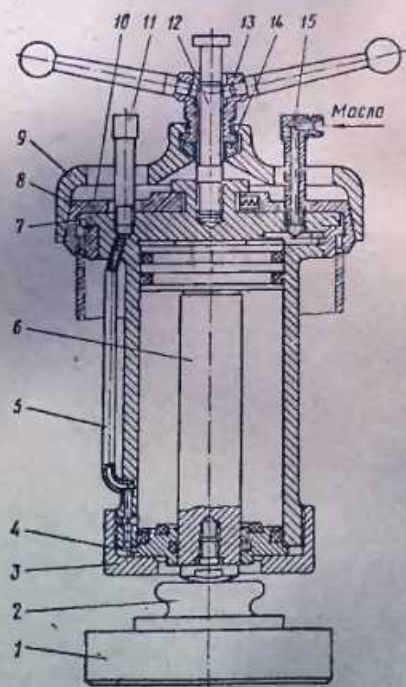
Приспособление для гидравлической выпрессовки гильзы:
